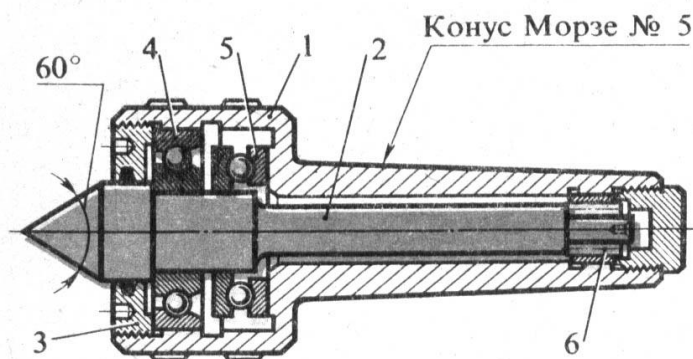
Центр, що обертається: 1 – корпус із хвостовиком, 2 – центр, 3 – кришка, 4, 5, 6 – підшипники
